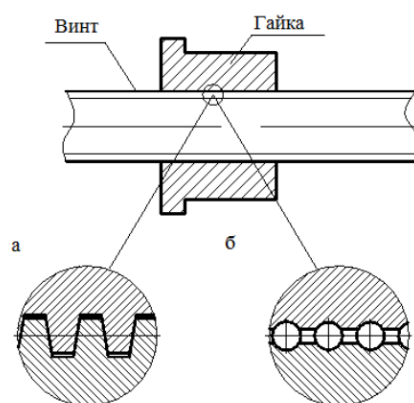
Передача винт-гайка: а – скольжения; б – качения
